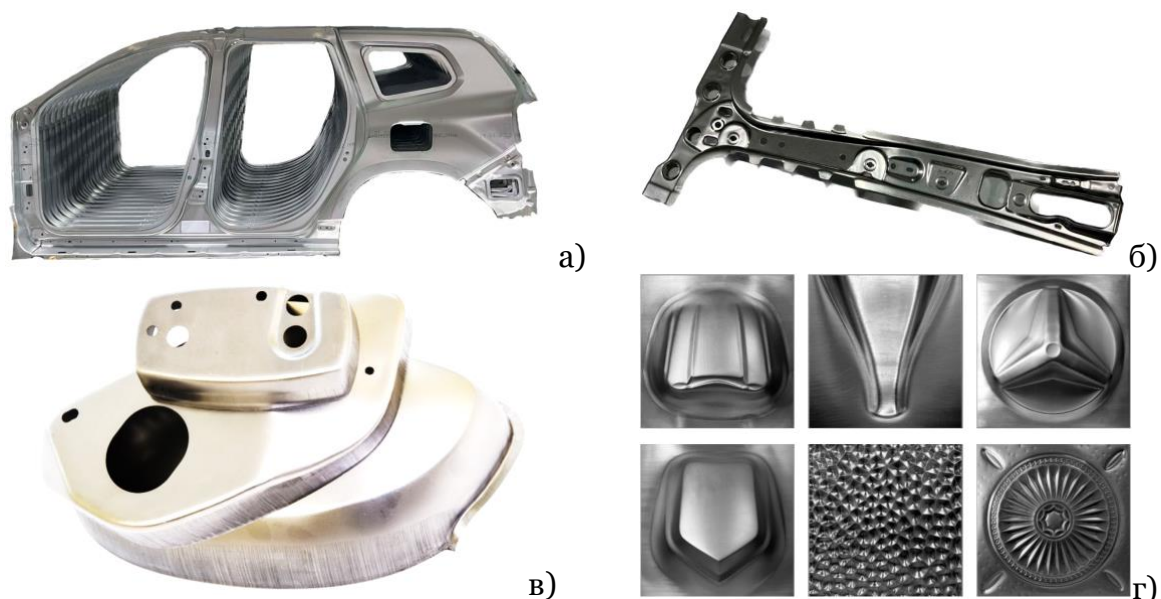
Примеры металлических листовых деталей: боковина автомобильного кузова (а) и боковая стойка автомобиля (б) [1], корпусная деталь (в) [2] и детали специального назначения (г) [3]
